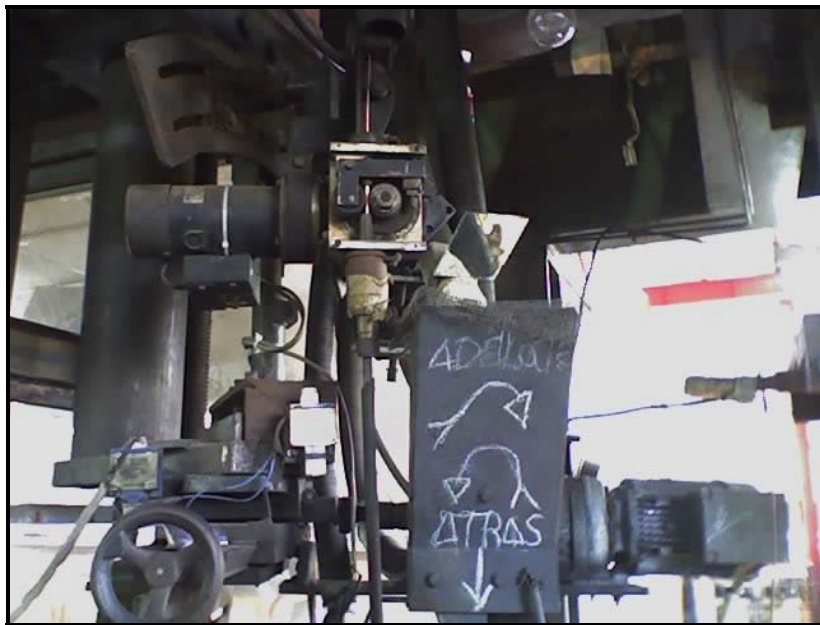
Se observa la base del cabezal de soldadura de la maquina formadora D.
